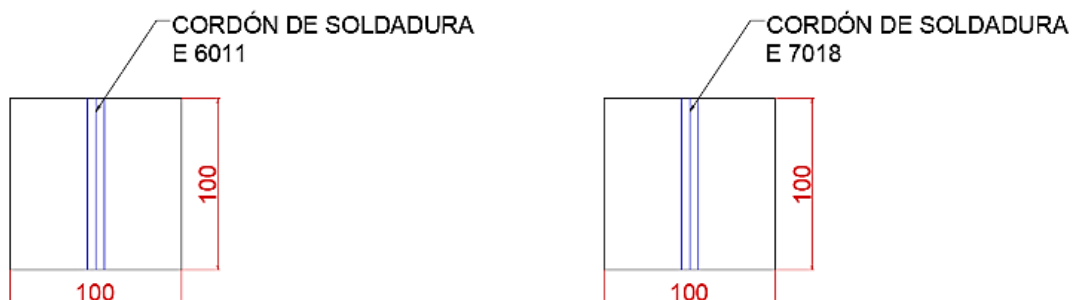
Pasos para realizar la práctica de soldadura SMAW
